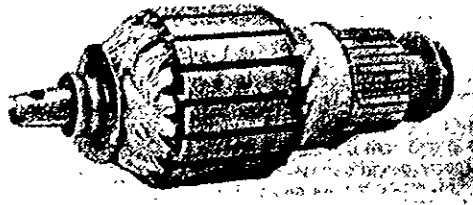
Rotor de un motor de inducción con embobinado nuevo.
